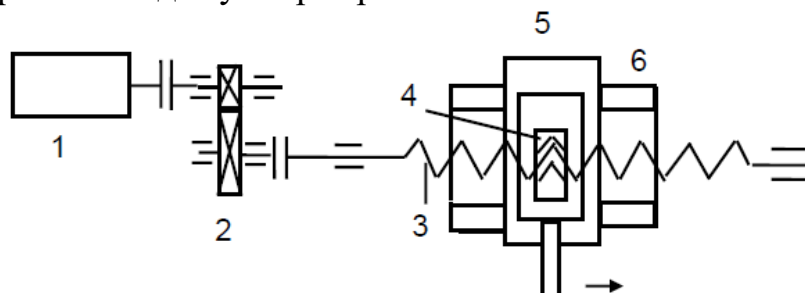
Кинематическая схема механизма: 1 – двигатель, 2 – редуктор, 3- ходовой винт, 4 – гайка, 5 – суппорт, 6 – направляющие.
